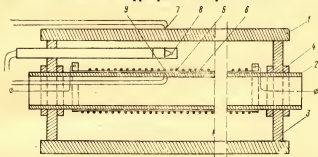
Схема нагревателя и его установки внутри асбестоцементной трубы
